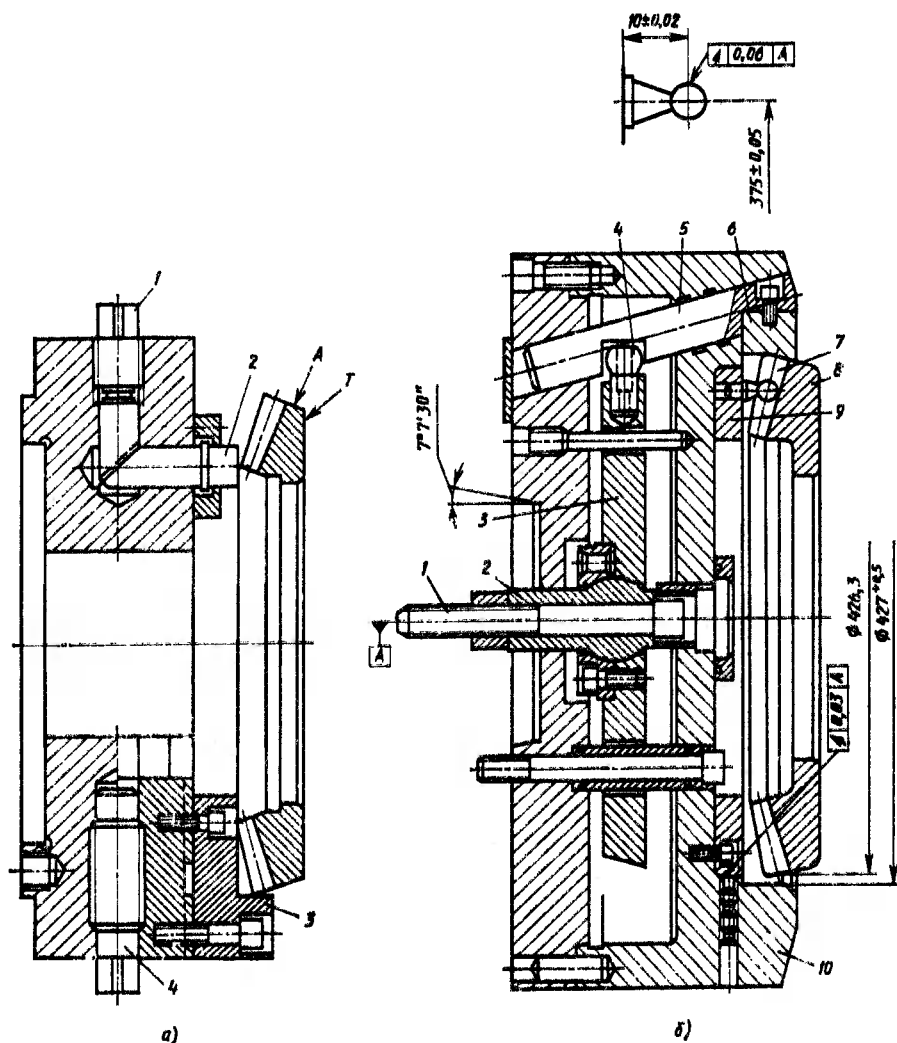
Схемы установки конических колес в зажимных приспособлениях
